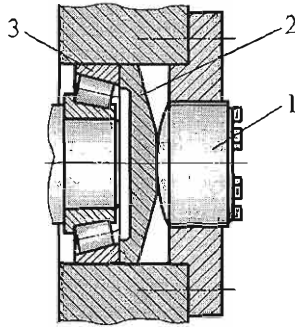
Осевое перемещение вала с червячным колесом винтами, установленными с обеих сторон вала
